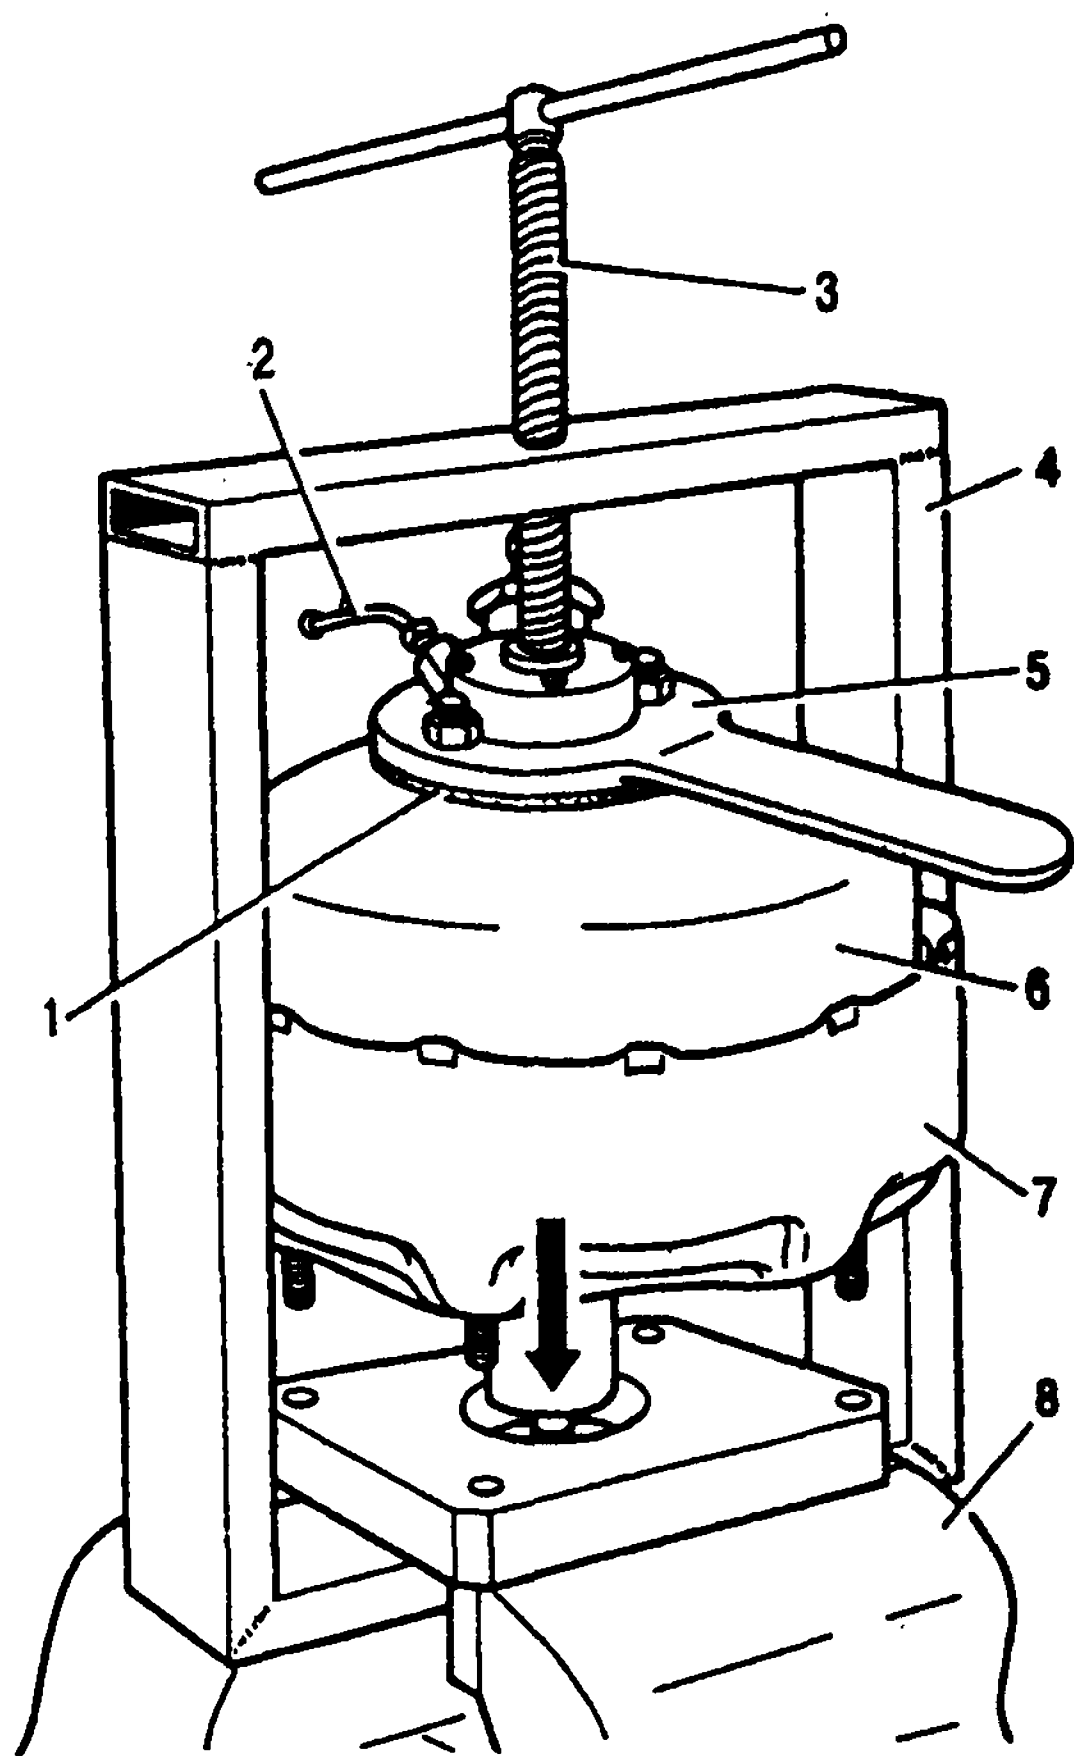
Приспособление для разборки и сборки усилителя: 1 - прокладка; 2 - вакуумная трубка; 3 - упорный винт; 4 - приспособление; 5 - ключ-заглушка; 6 - крышка вакуумного усилителя; 7 - корпус вакуумного усилителя; 8 - тиски
